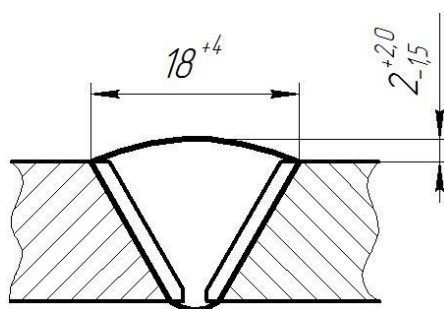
Конструктивные элементы сварного шва
